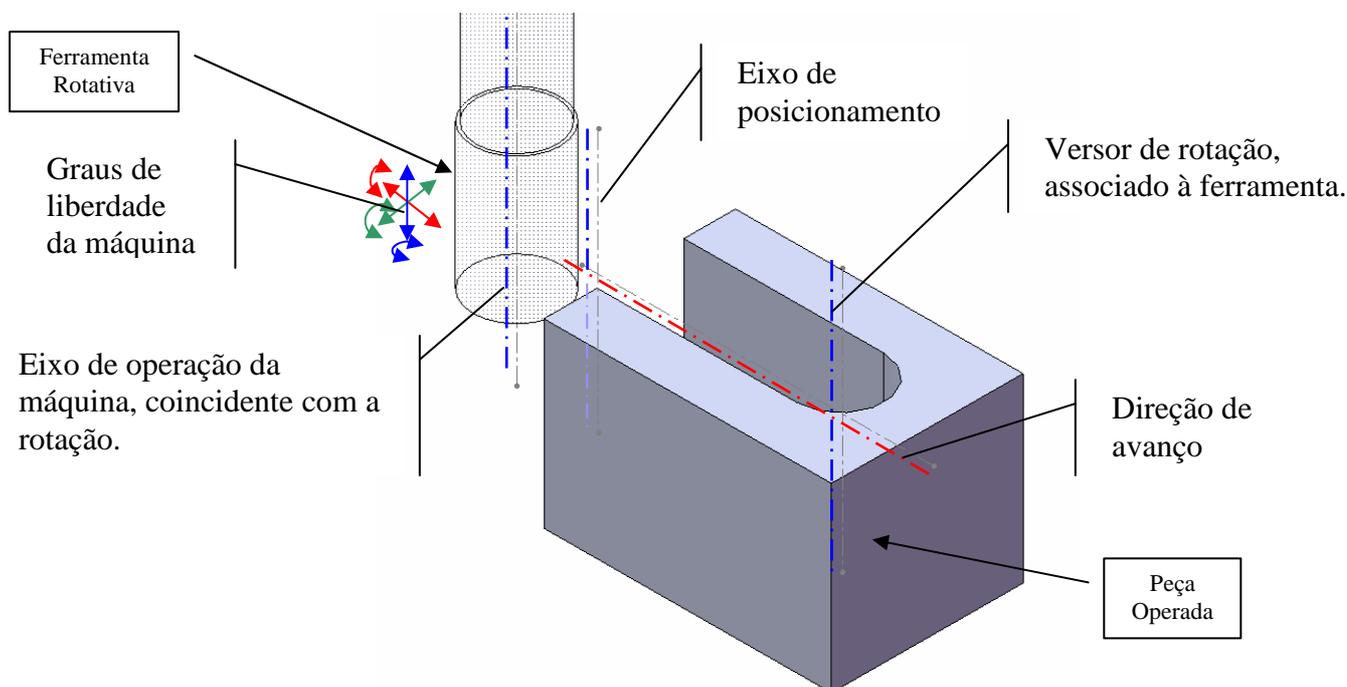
Exemplo de visualização da cinemática da máquina-ferramenta necessária à usinagem da feature.
